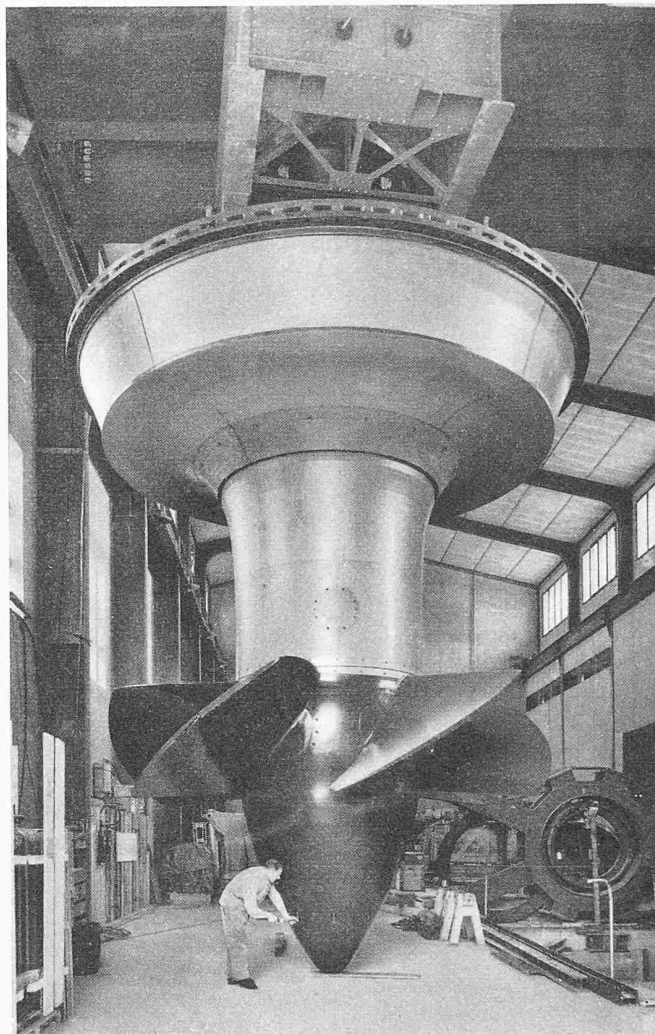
(oben). Laufrad mit Lagermantel und Turbinendeckel von dem Einbau im Maschinenhaus. 21. April 1952
